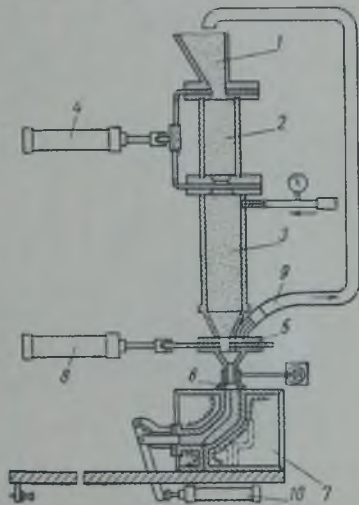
Схема пескодувной установки для изготовления оболочковых стержней
